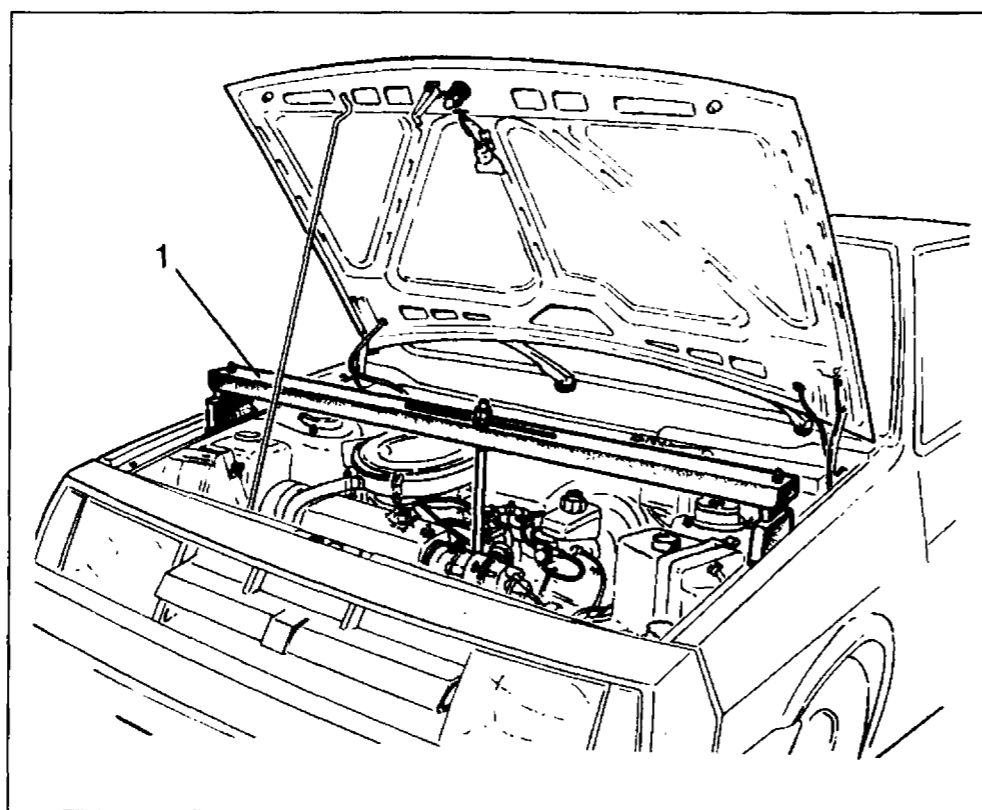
Установка поперечины 67.7820.9514 для поддержания силового агрегата:
